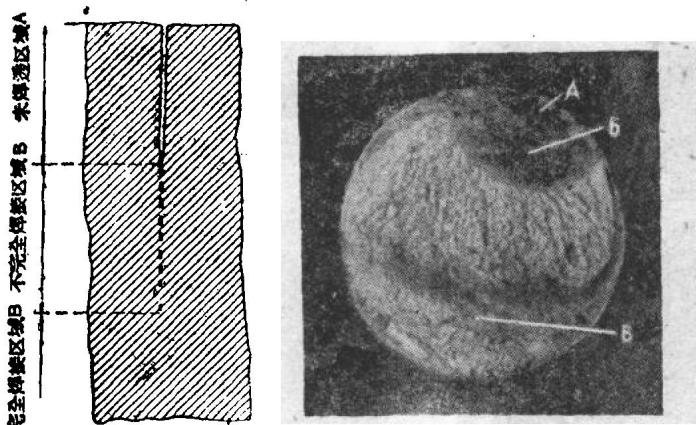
右用噴咀局部被堵塞的焊炬所焊接的接头的断口；
